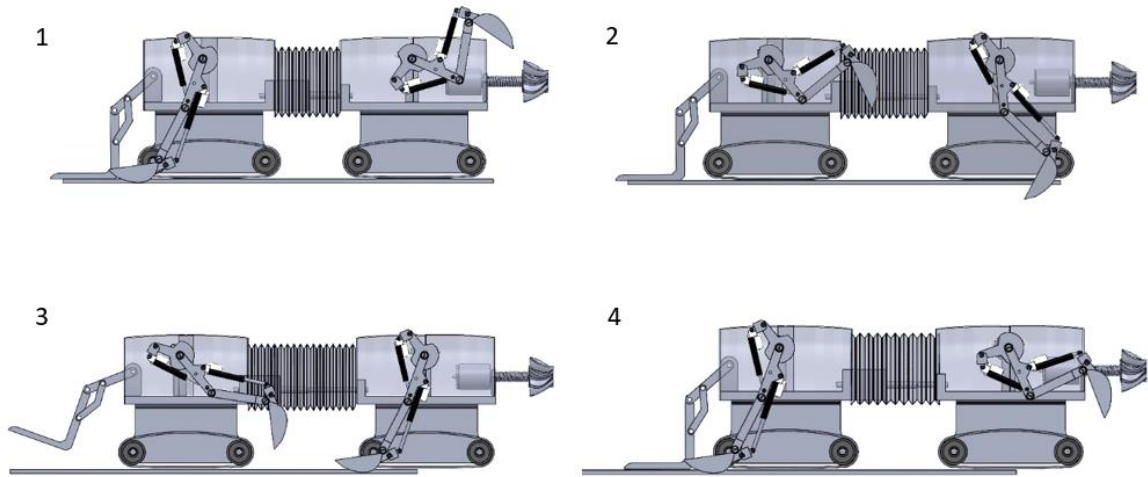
Robot ve Kol mekanizmasının CAD Modeli (CAD Model of Robot and Arm mechanism)
